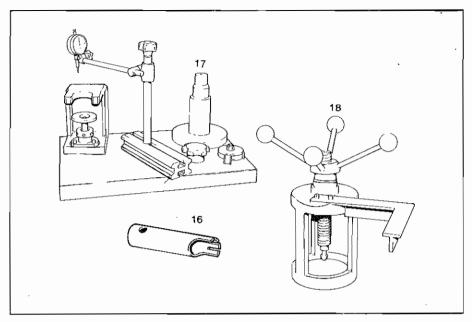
Attrezzi speciali telaio Speciel tools, frame
